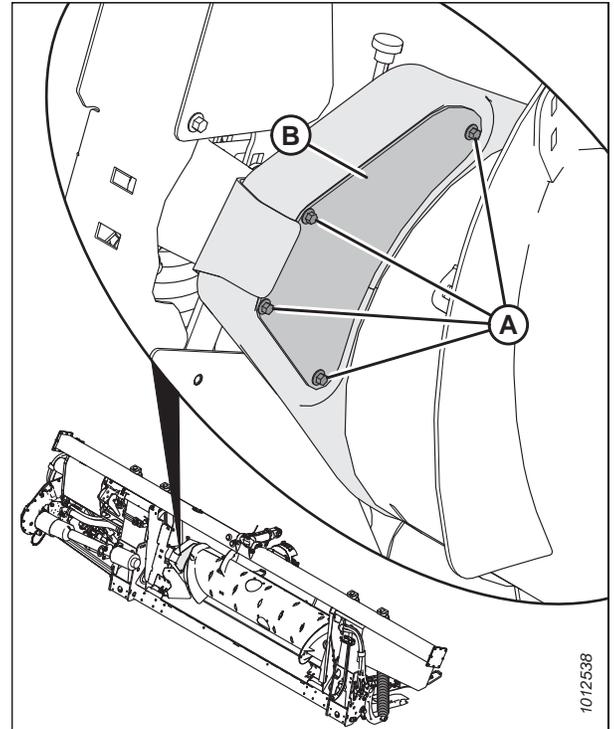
Côté gauche de l'entraînement de la vis – vue arrière
